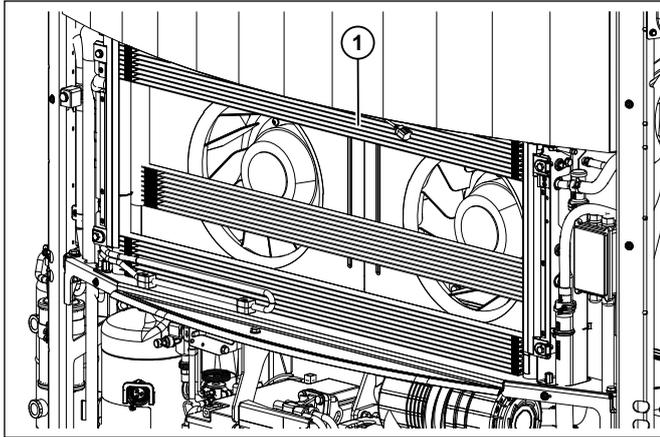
Очистка конденсатора (S.CU dc90, S.CU d80 и S.CU e80)
